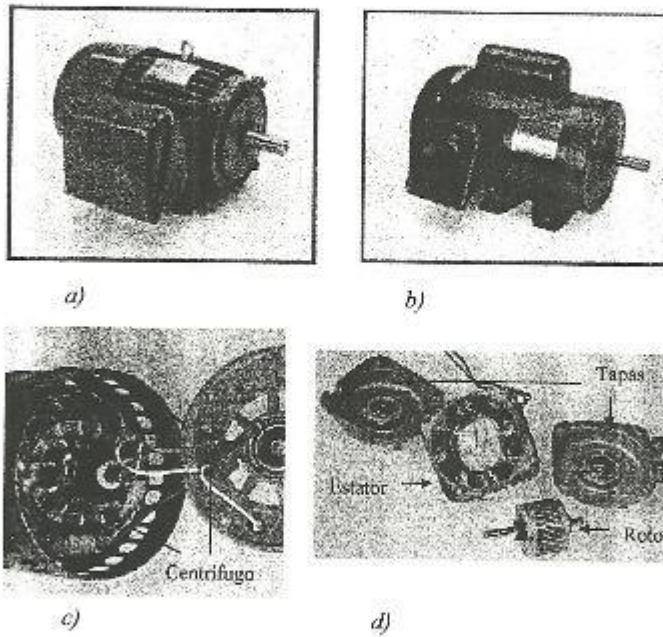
Motor monofásico de inducción a) Motor de fase partida b) Motor con condensador c) Motor con la parte giratoria del interruptor centrifugo d) Despiece de un motor monofásica
